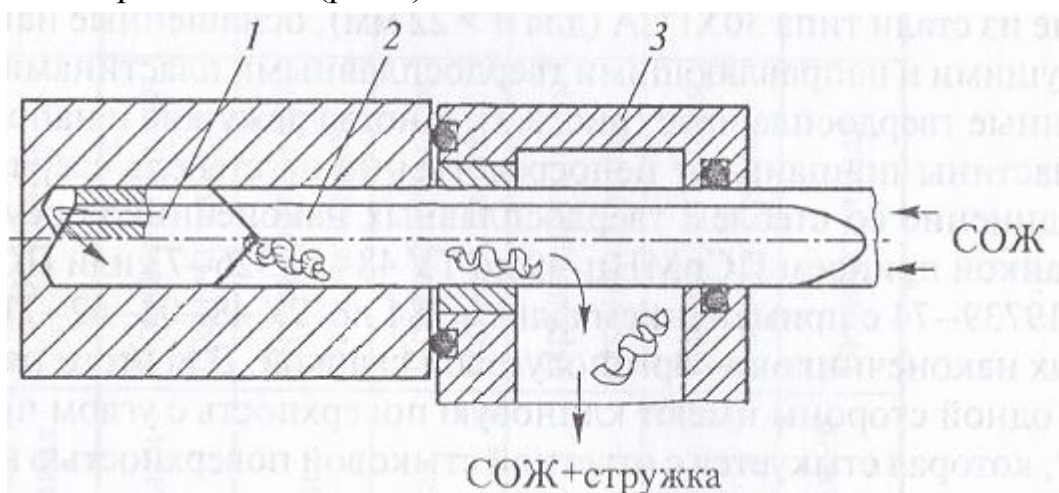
Схема сверления глубоких отверстий ружейным сверлом
